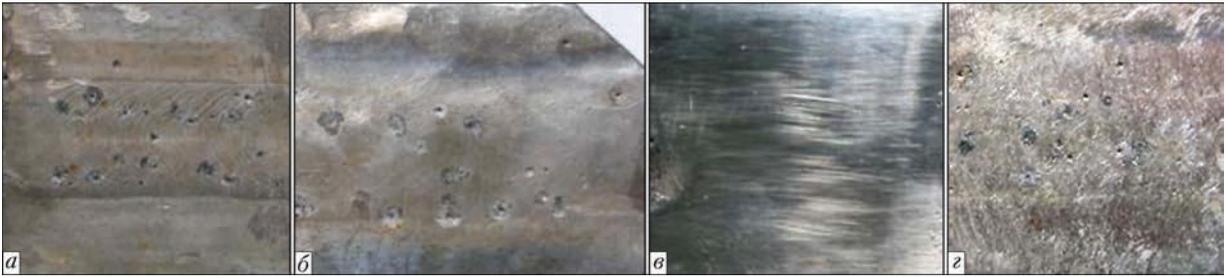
Поверхность сварных соединений шлифованной нержавеющей стали, испытанных на питтинговую коррозию после сварки (а), проковки (б), полировки (в), торцевого трения (з)
